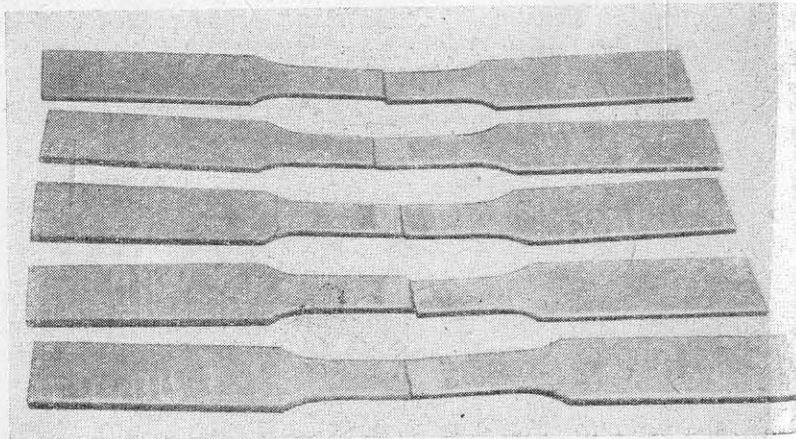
Образцы на разрыв, сваренные автоматической сваркой.
